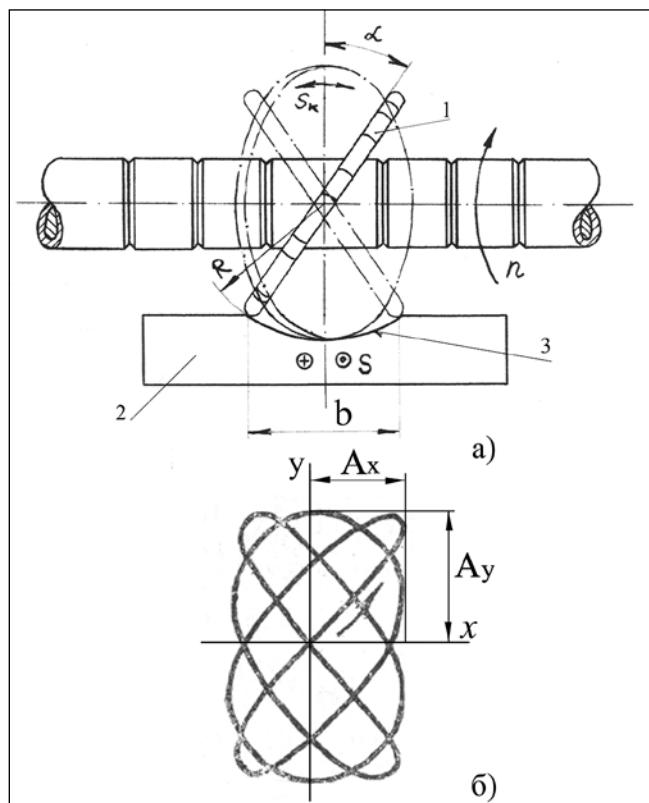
Фрезерование наклонной дисковой фрезой — а), траектория движения зубьев — б)
